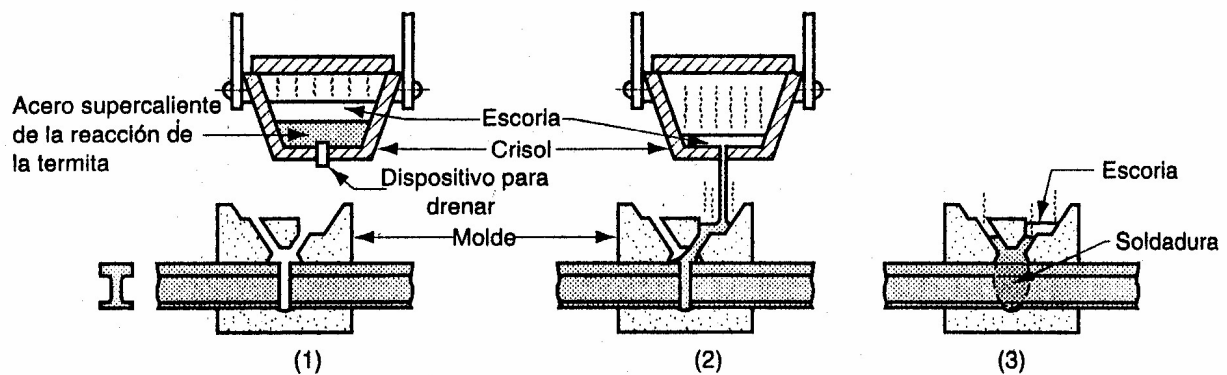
Soldadura de termita: (1) termita encendida; (2) metal súper calentado que se drena del crisol fluye dentro de un molde y (3) el metal se solidifica para producir una unión soldada.
